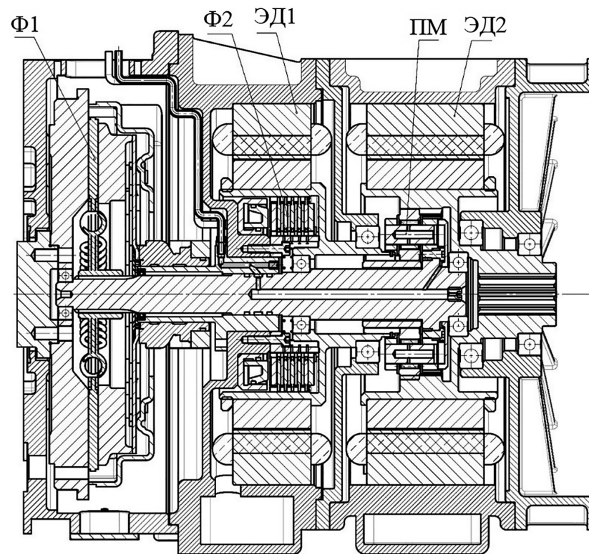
Продольный разрез мехатронного модуля ГСУ автомобиля MAZ-5340C5Г1: 1 — сцепление (Ф1); 2 — электродвигатель-генератор ЭД1; 3 — планетарный механизм (ПМ); 4 — фрикцион Ф2; 5 — электродвигатель-генератор ЭД2; ДВС и автоматизированная КП
